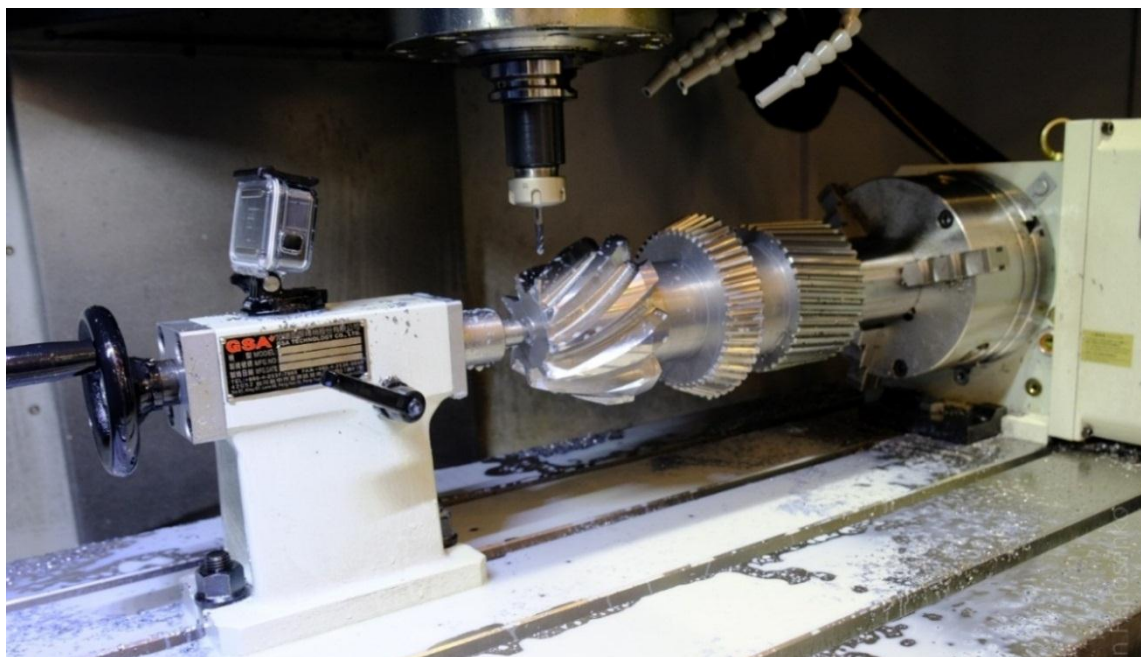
Високоєфективне оброблення деталі "вал зубчастий"
